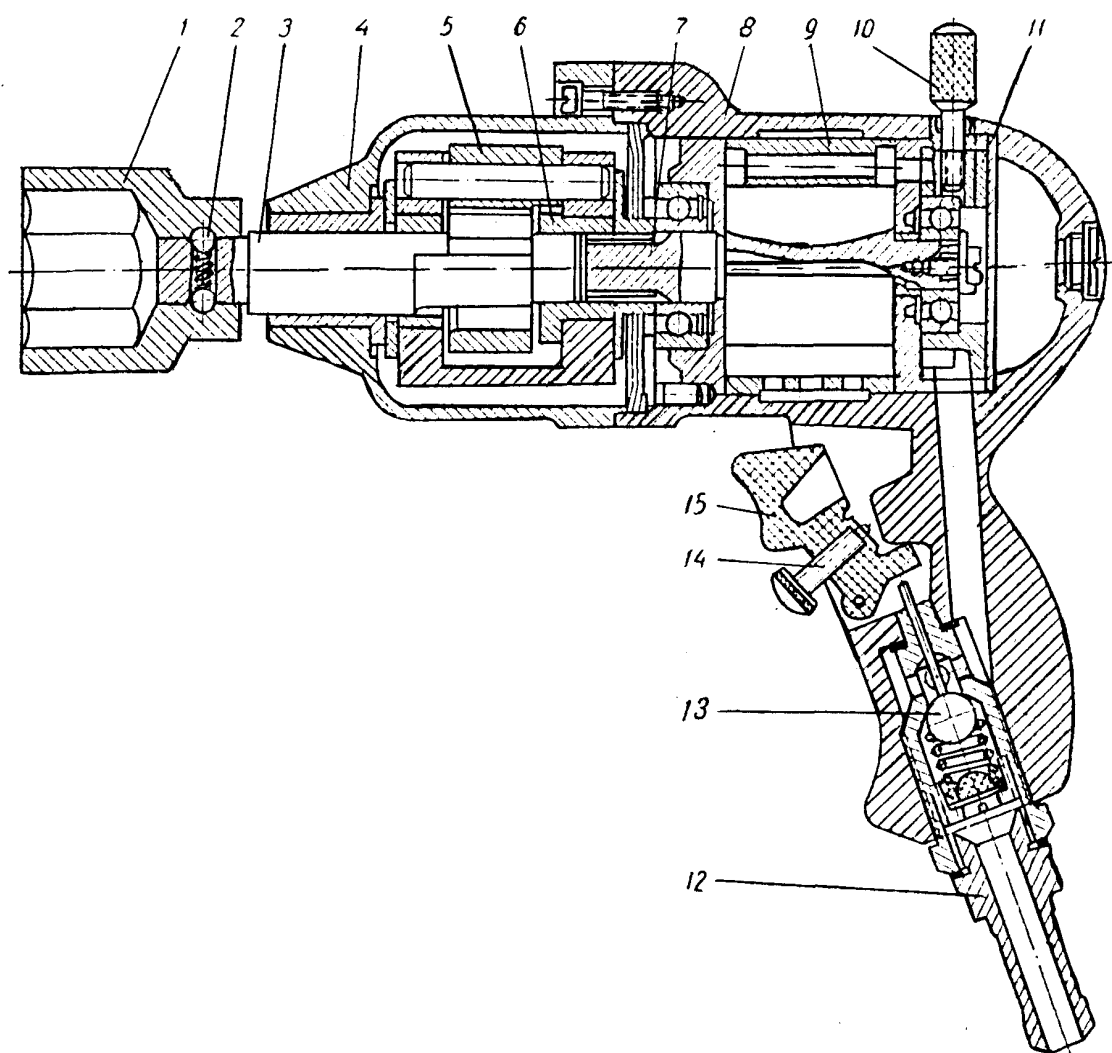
Пневматичний реверсивний гайковерт П-3130: 1 – змінна торцева головка; 2 – кулька торцевої головки; 3 – шпindel, 4 – корпус ударного механізму; 5 – ударний механізм; 6 – шліцьова муфта; 7 – вал ротора реверсивного ротаційного пневматичного двигуна; 8 – корпус ротаційного пневматичного двигуна; 9 – ротаційний пневматичний двигун; 10 – палець повітрянорозподільного кільця; 11 – повітрянорозподільне кільце, 12 – штуцер повітрянопроводного шлангу; 13 – пусковий пристрій; 14 – гвинт пускового курка; 15 – пусковий курок
